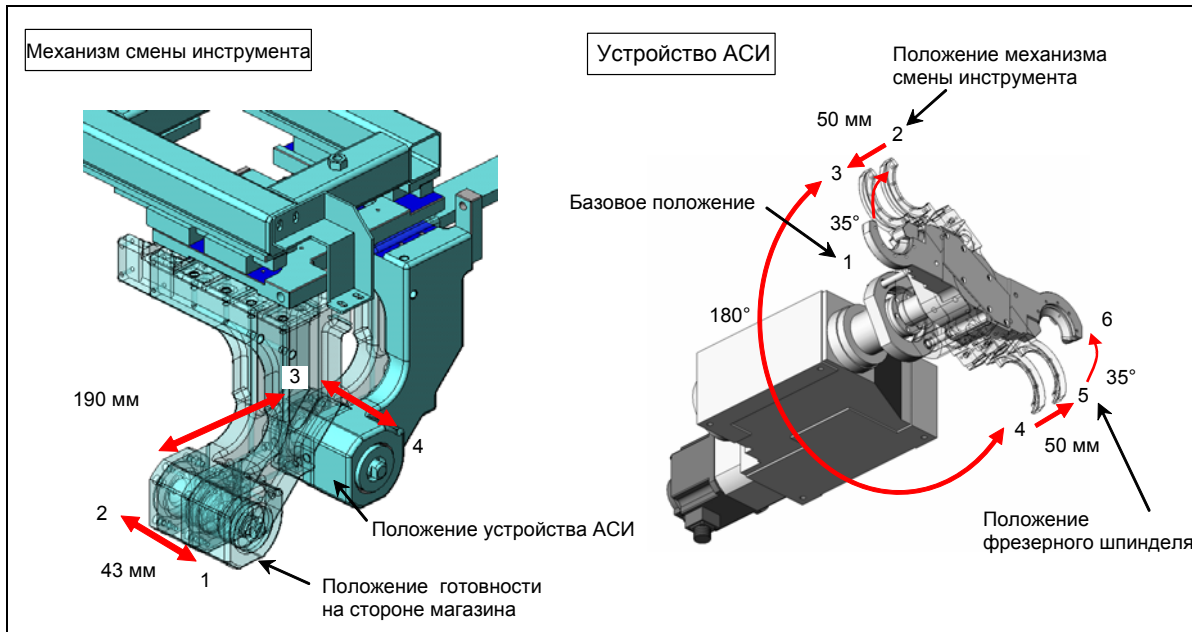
Перемещения устройства АСИ и механизма смены инструмента (для станка с магазином на 36 инструментов)
